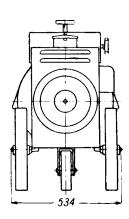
Massbild des Schweissumformers EW-21u
